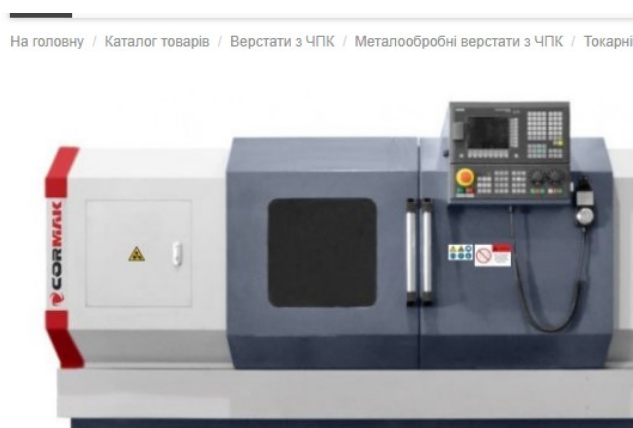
Токарний верстат мод. Cormak CNC 620x1500 2000.
